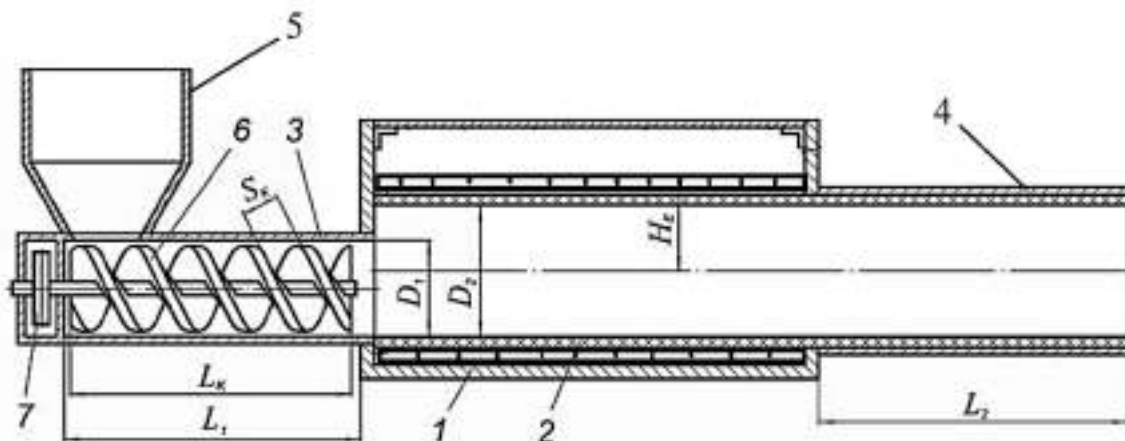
Схема індукційного пристрою безперервної дії для термообробки зернового матеріалу: 1 – робоча камера, 2 – індуктор, 3 – завантажувальний трубопровід, 4 – випускний трубопровід, 5 – завантажувальний бункер, 6 – шнек, 7 – приводний вузол
